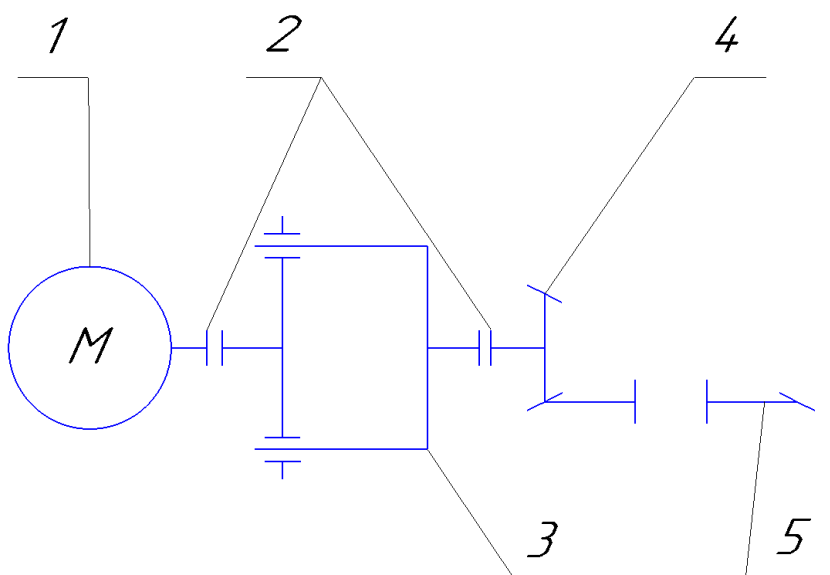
Кинематическая схема резьбонарезной РМ с ВЗП
